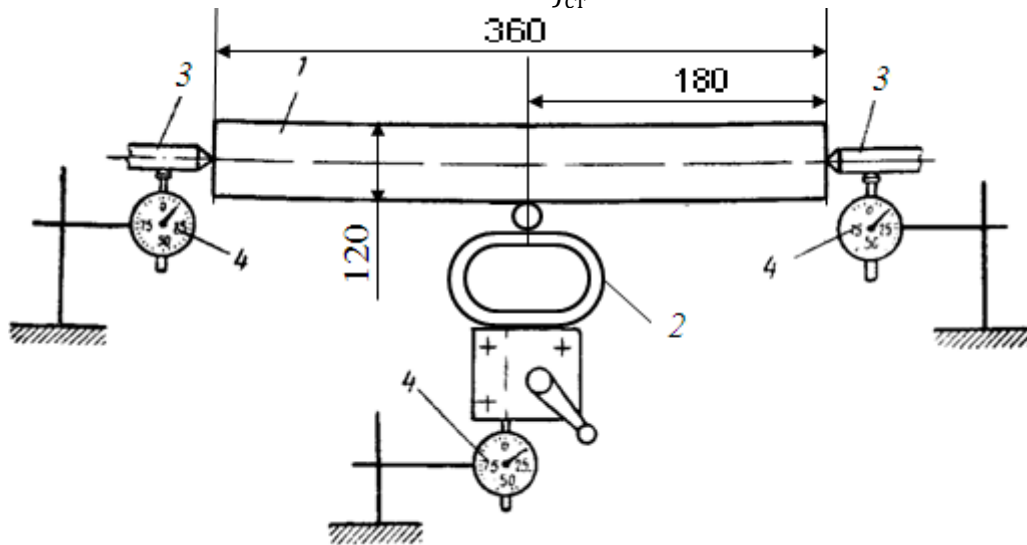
Схема установки для измерения податливости токарного станка при обработке заготовки в центрах: 1 – заготовка; 2 – динамометр; 3 – центры; 4 – индикаторы.
